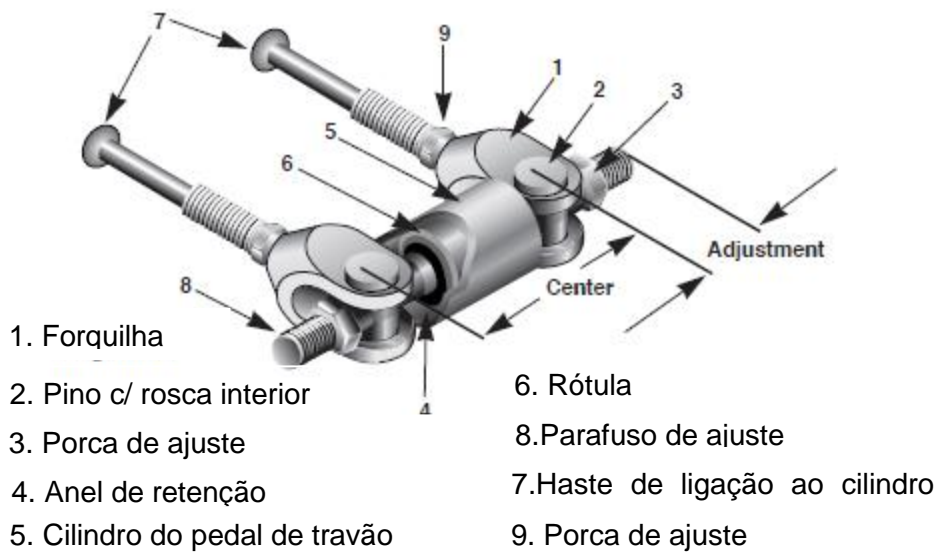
Exemplo de barra de balanço (fonte: tiltonracing).
